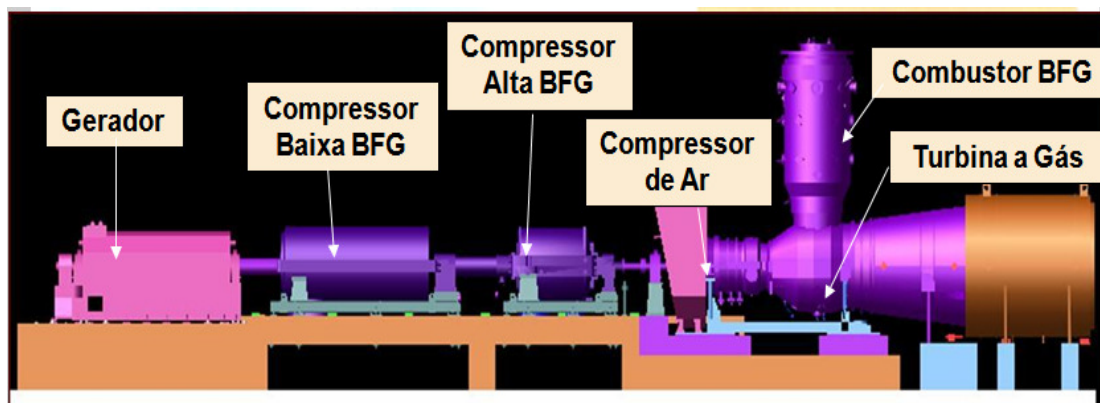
Ilustração do conjunto de geração da turbina GT11N2 LBTU Alstom
